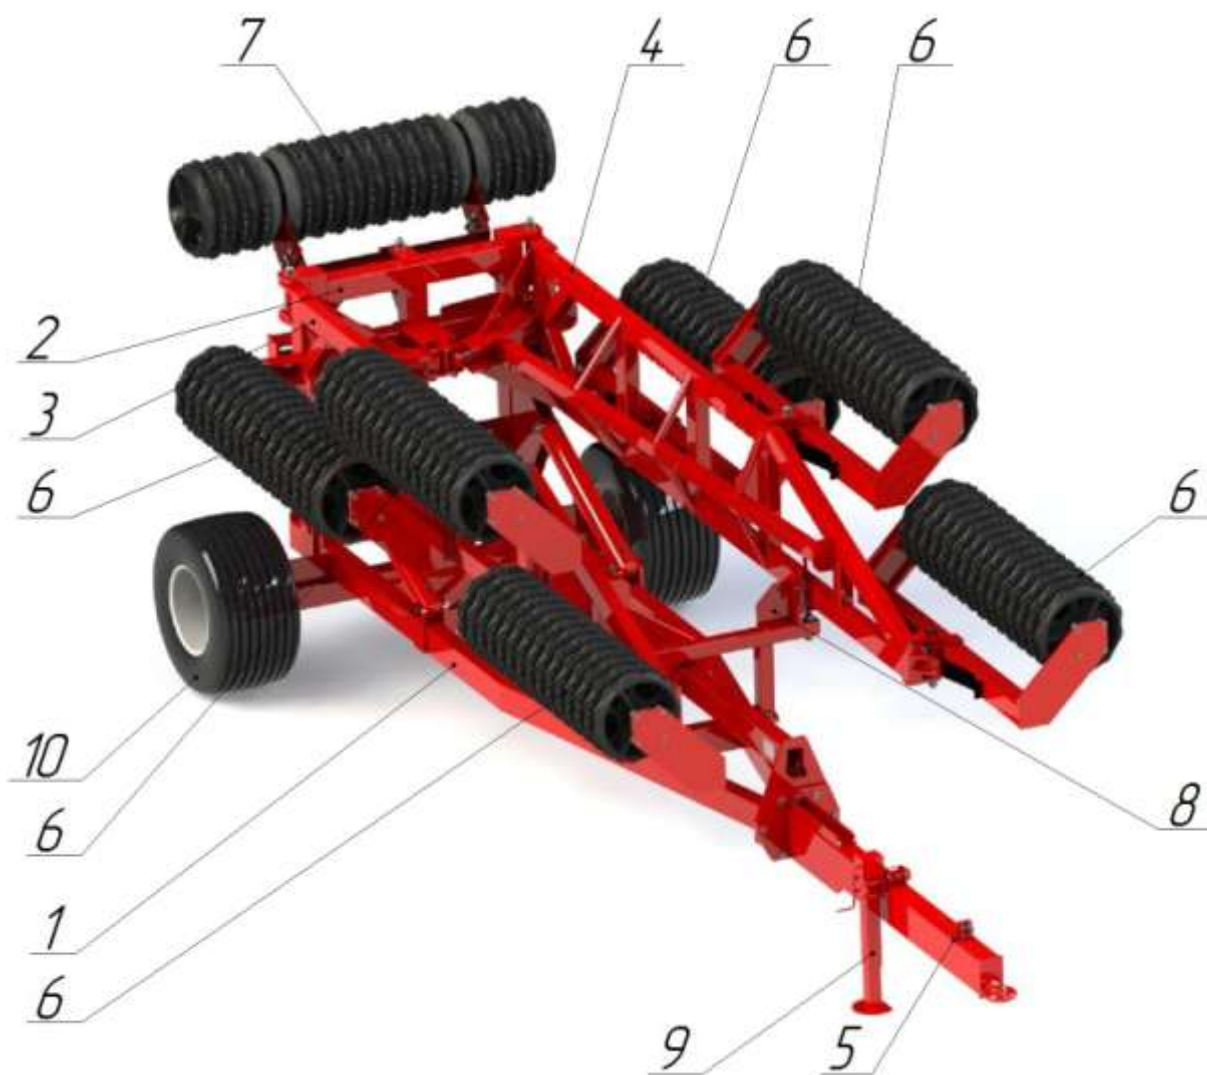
Общий вид катка кольчато-зубчатого Булава КЗ-12,4
